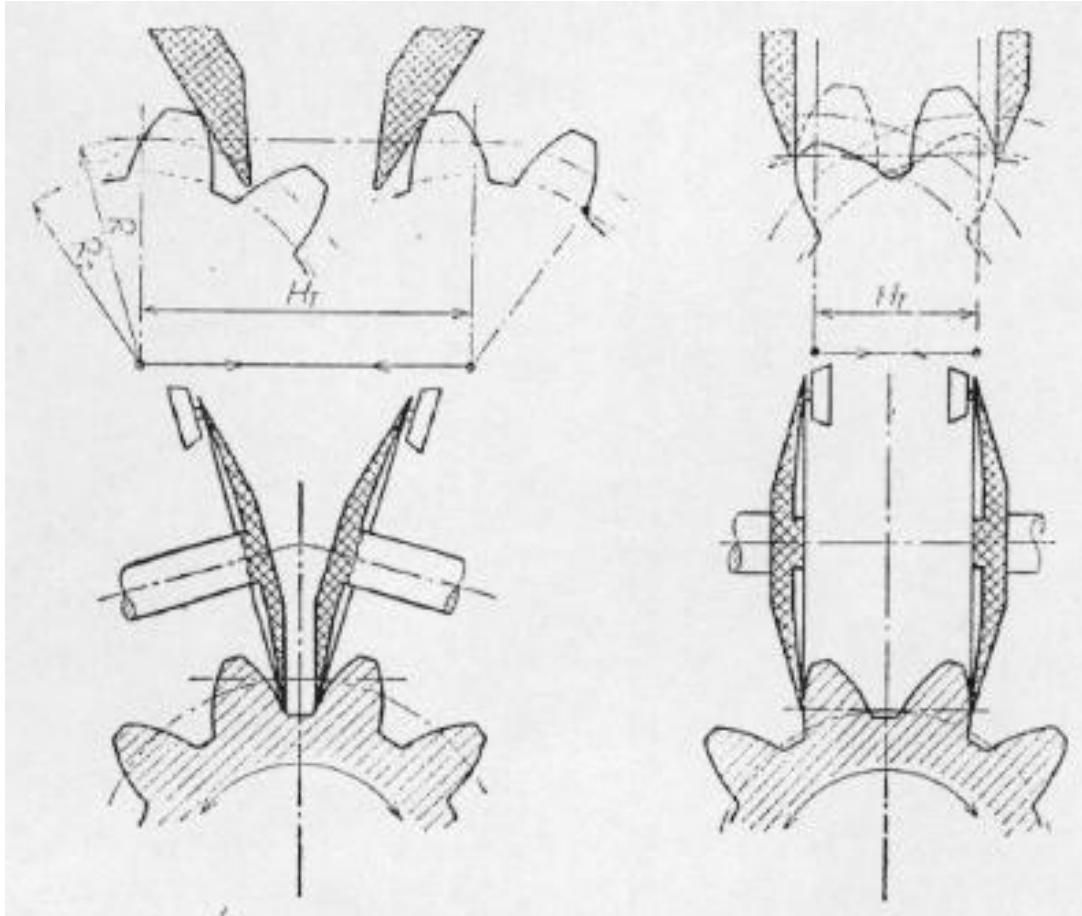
Broušení ozubení tvarovými kotouči [36]
